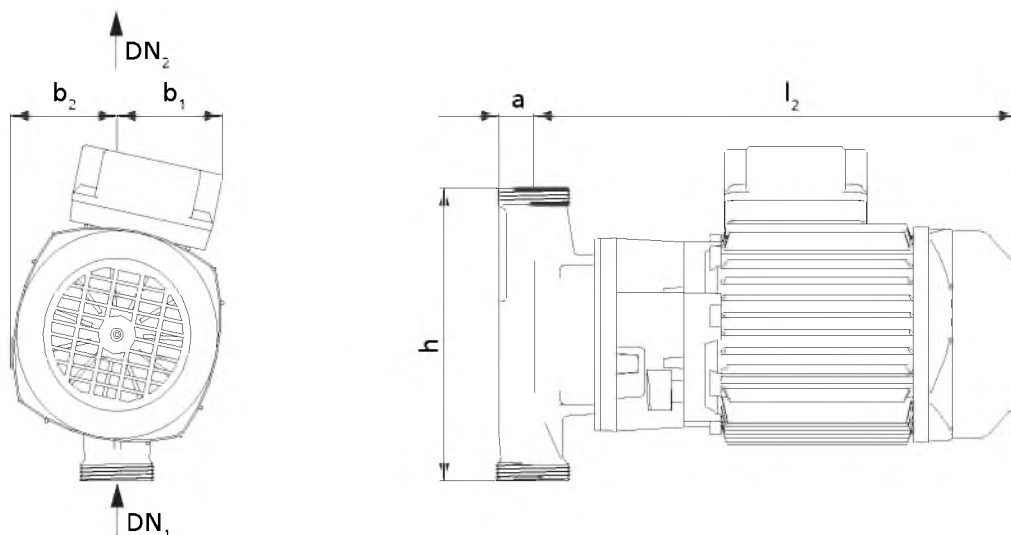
Размеры насосного агрегата с резьбовым соединением, типоразмер < 032-032-100
